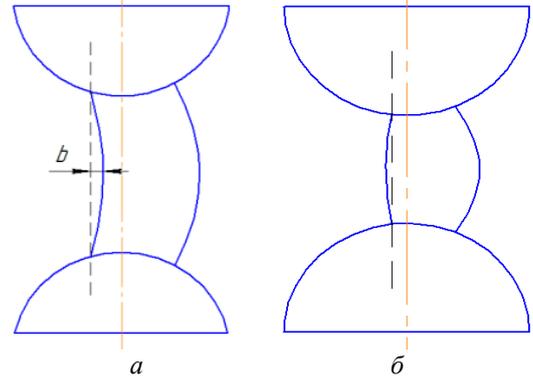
Появление продольного изгиба (а) и бочкообразования (б) в процессе осадки выпуклыми радиусными бойками с эксцентриситетом нагрузки: b – величина прогиба заготовки в процессе осадки
